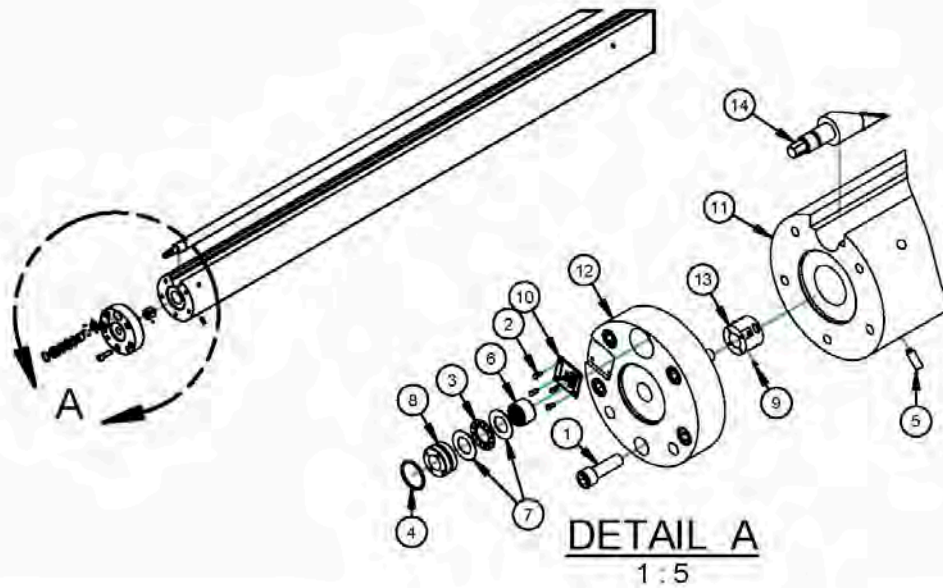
Bohrstangenbaugruppe (P/N 81629)
